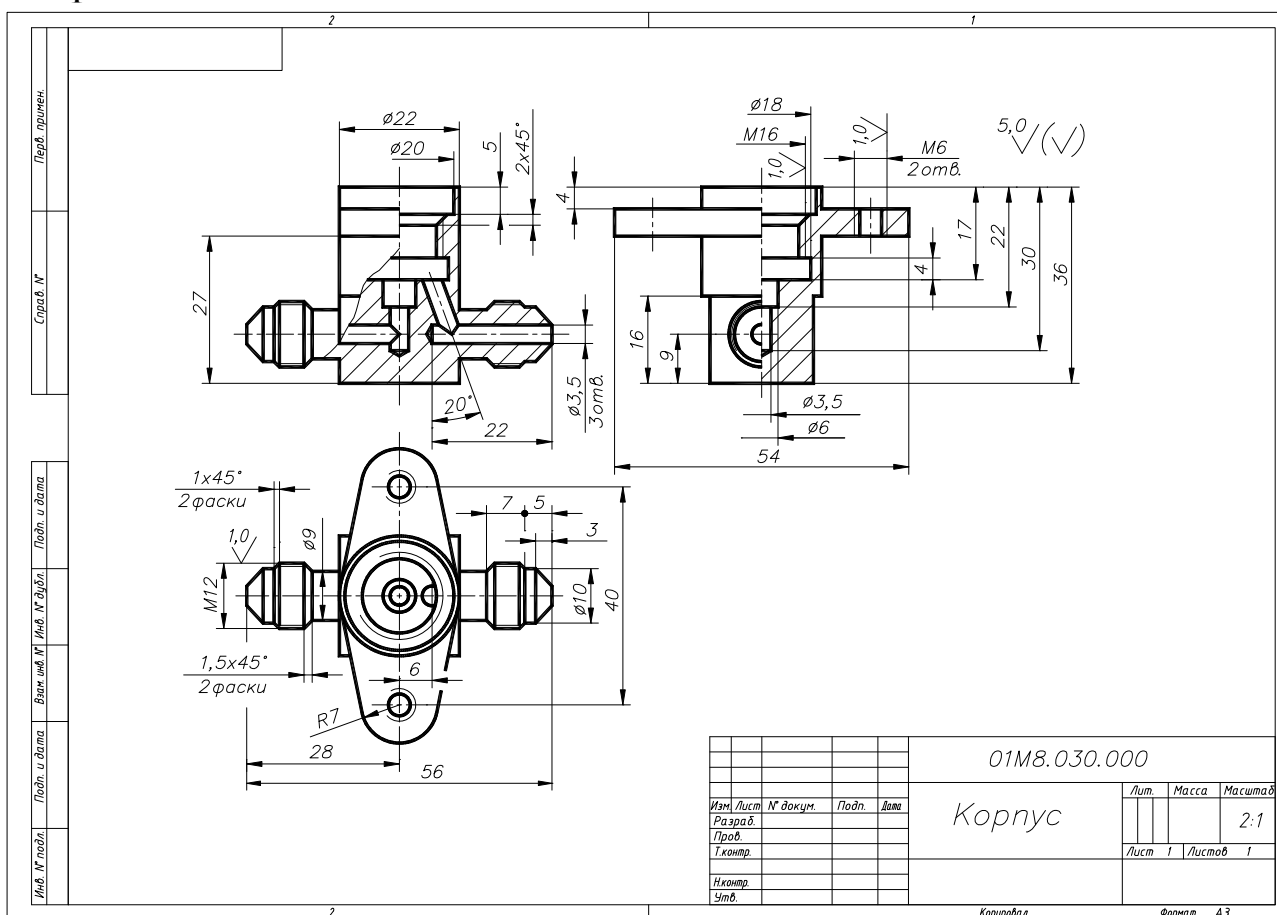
Чертеж детали «Корпус 01M8.030.000».
